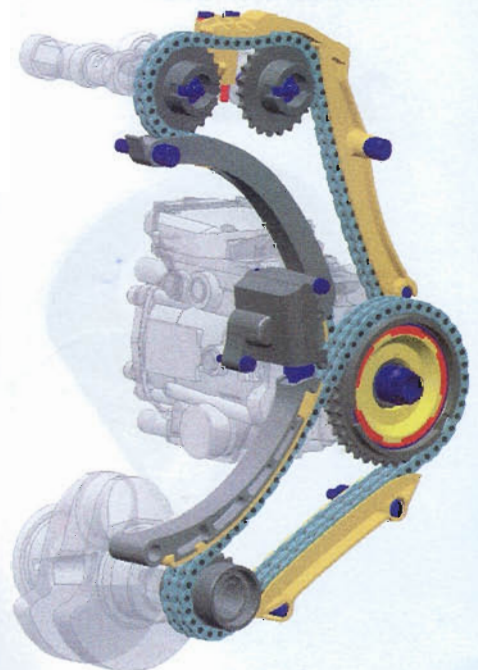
Kettentrieb für Einspritzpumpe und Nockenwellen
